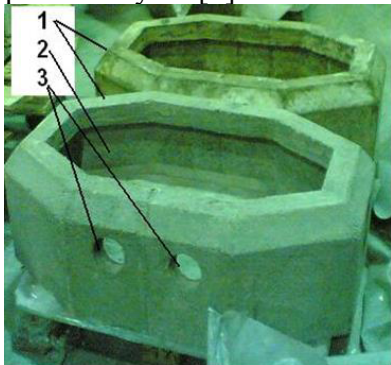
Приёмник жидкого металла из сталеразливочного ковша: 1 - приёмники; 2 – отверстие для прохождения металла из СРК; 3 – отверстия для распределения потоков металла
